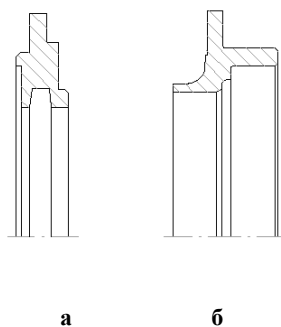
Посадочное место под уплотнения в крышке подшипника:
